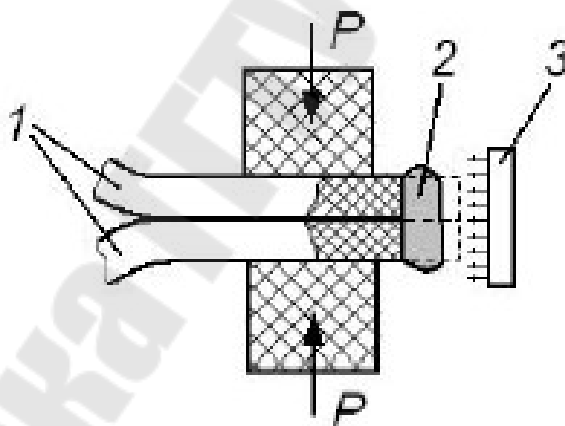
Схема сварки инфракрасным с получением рантовых швов: 1 – свариваемые пленки; 2 – сварной шов; 3 – ИК - излучатель
